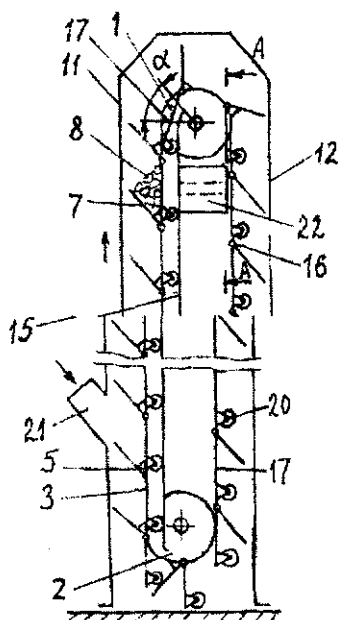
Вертикальный элеватор для кускового груза (вид сбоку, без боковой стенки)
